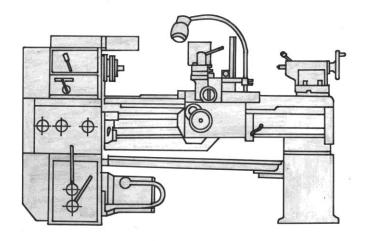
Токарно-винторезный станок модели ИТ-1Е
